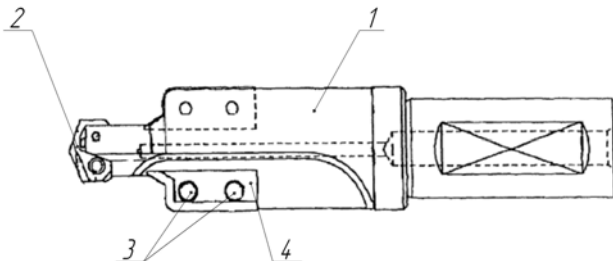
Свердло-зенківка фірми Hayes Lemmerz International
